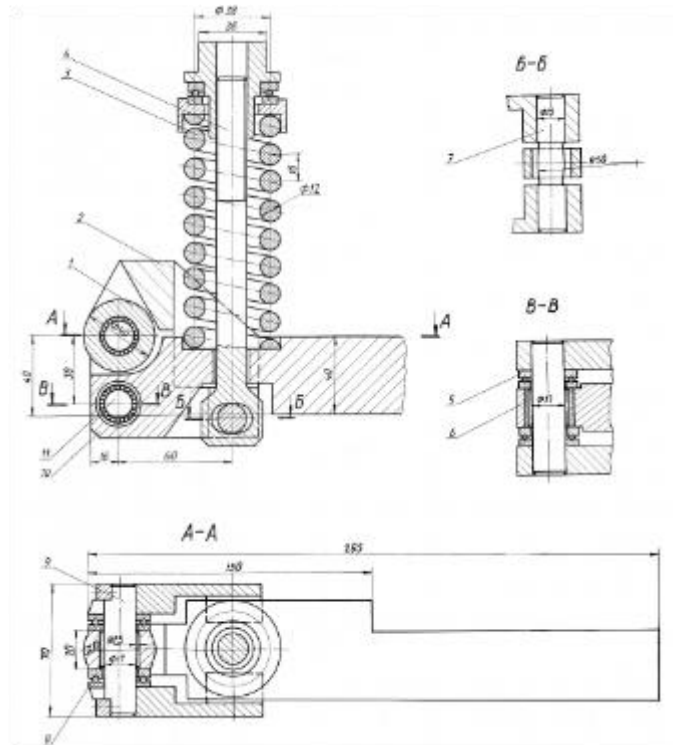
Пристрій для обкатування роликом із стабілізацією зусилля обкатування: 1-ролик; 2-важіль; 3-пружина; 4-тяги; 5,6-підшипник; 7-вісь; 8-підшипник; 9-вісь; 10-корпус; 11-вісь
